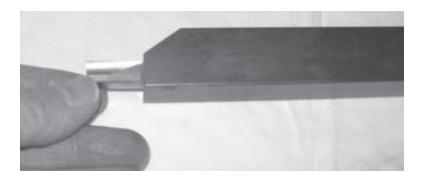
Placez l'outil à dresser dans le porte-outil (voir la photo). Serrez les vis de fixation sur le porte-outil.
